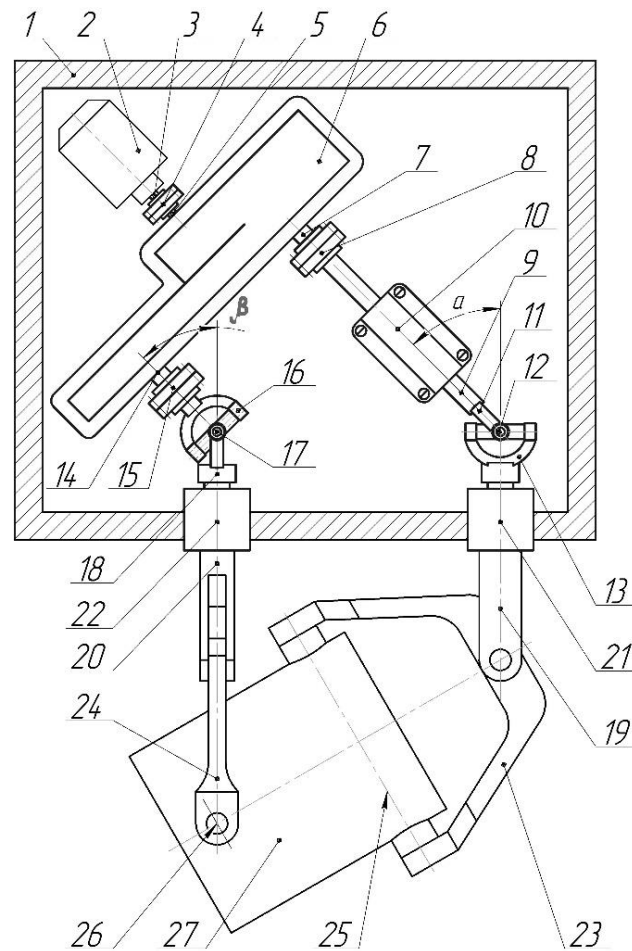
Машина для обробки деталей з двома ведучими валами
